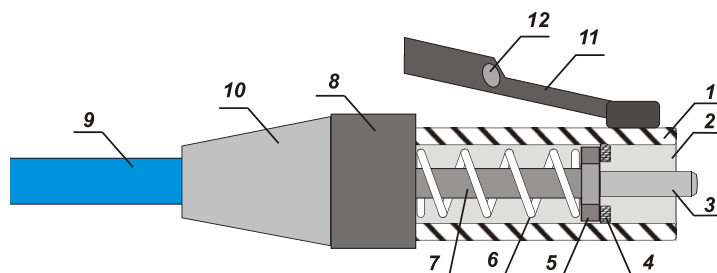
Основные конструктивные элементы вилки LC классического дизайна: 1 – корпус; 2 – установочное гнездо; 3 – центрирующий наконечник; 4 – упор для оправки наконечника; 5 – оправка наконечника; 6 – нажимная пружина; 7 – защитная трубка; 8 – заглушка; 9 – оптический кабель; 10 – хвостовик; 11 – рычаг защелки; 12 – рабочий элемент защелки
